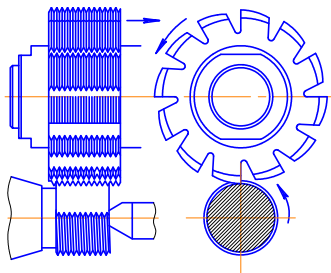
нарезание короткой остроугольной резьбы гребенчатой групповой фрезой на резьбофрезерном станке.
